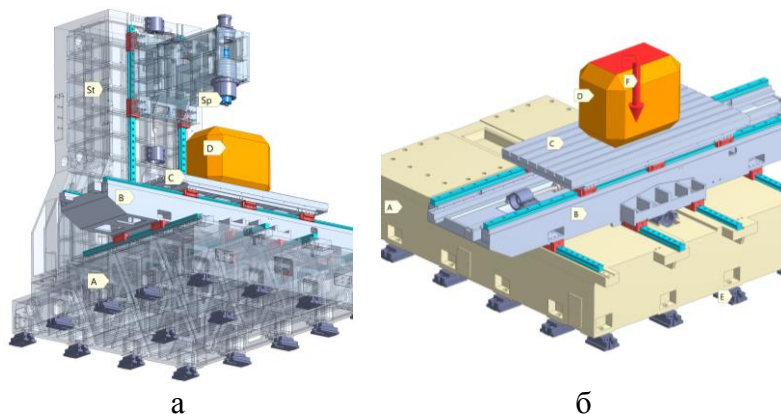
Вертикально-фрезерный станок (ВФС) с чугунной станиной А (а) и крестовый стол (салазки В + плита С) на фибробетонной станине А (б): D – образ заготовки; F – вертикальная сила; St – стойка для вертикальных перемещений бабки со шпиндельным узлом Su
